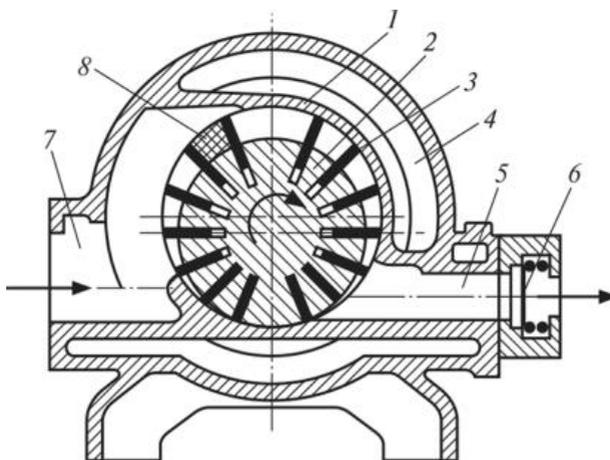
Роторно-пластинчатый компрессор: 1- корпус(статор); 2- ротор; 3- пластины; 4- водяная рубашка; 5- нагнетательный патрубок; 6- клапан; 7- всасывающий патрубок; 8- сектор переменного сечения
